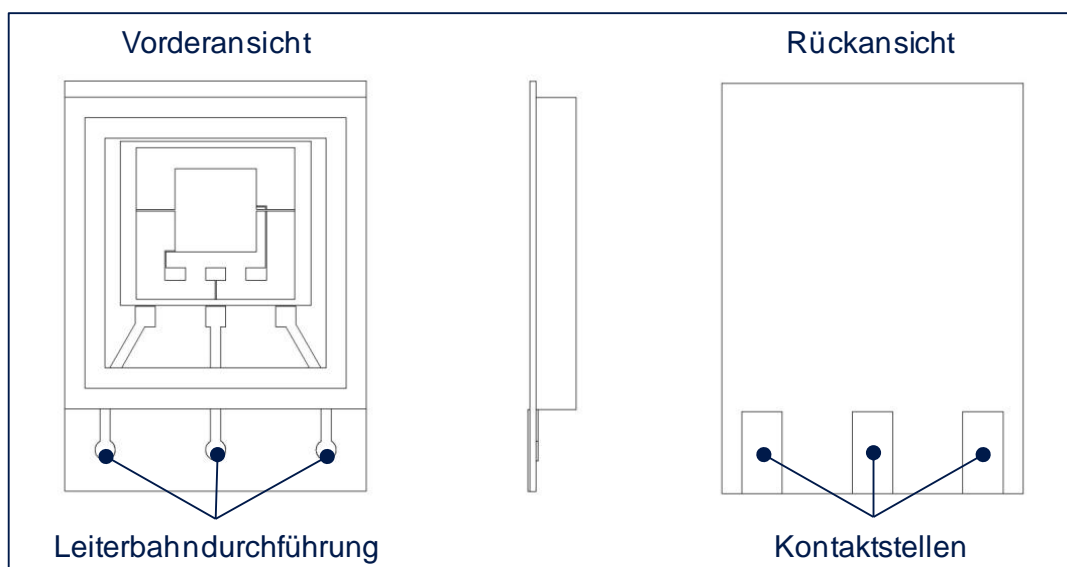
Vorder- und Rückansicht der Spiegelbaugruppe mit produktseitiger MeMo-Schnittstelle
